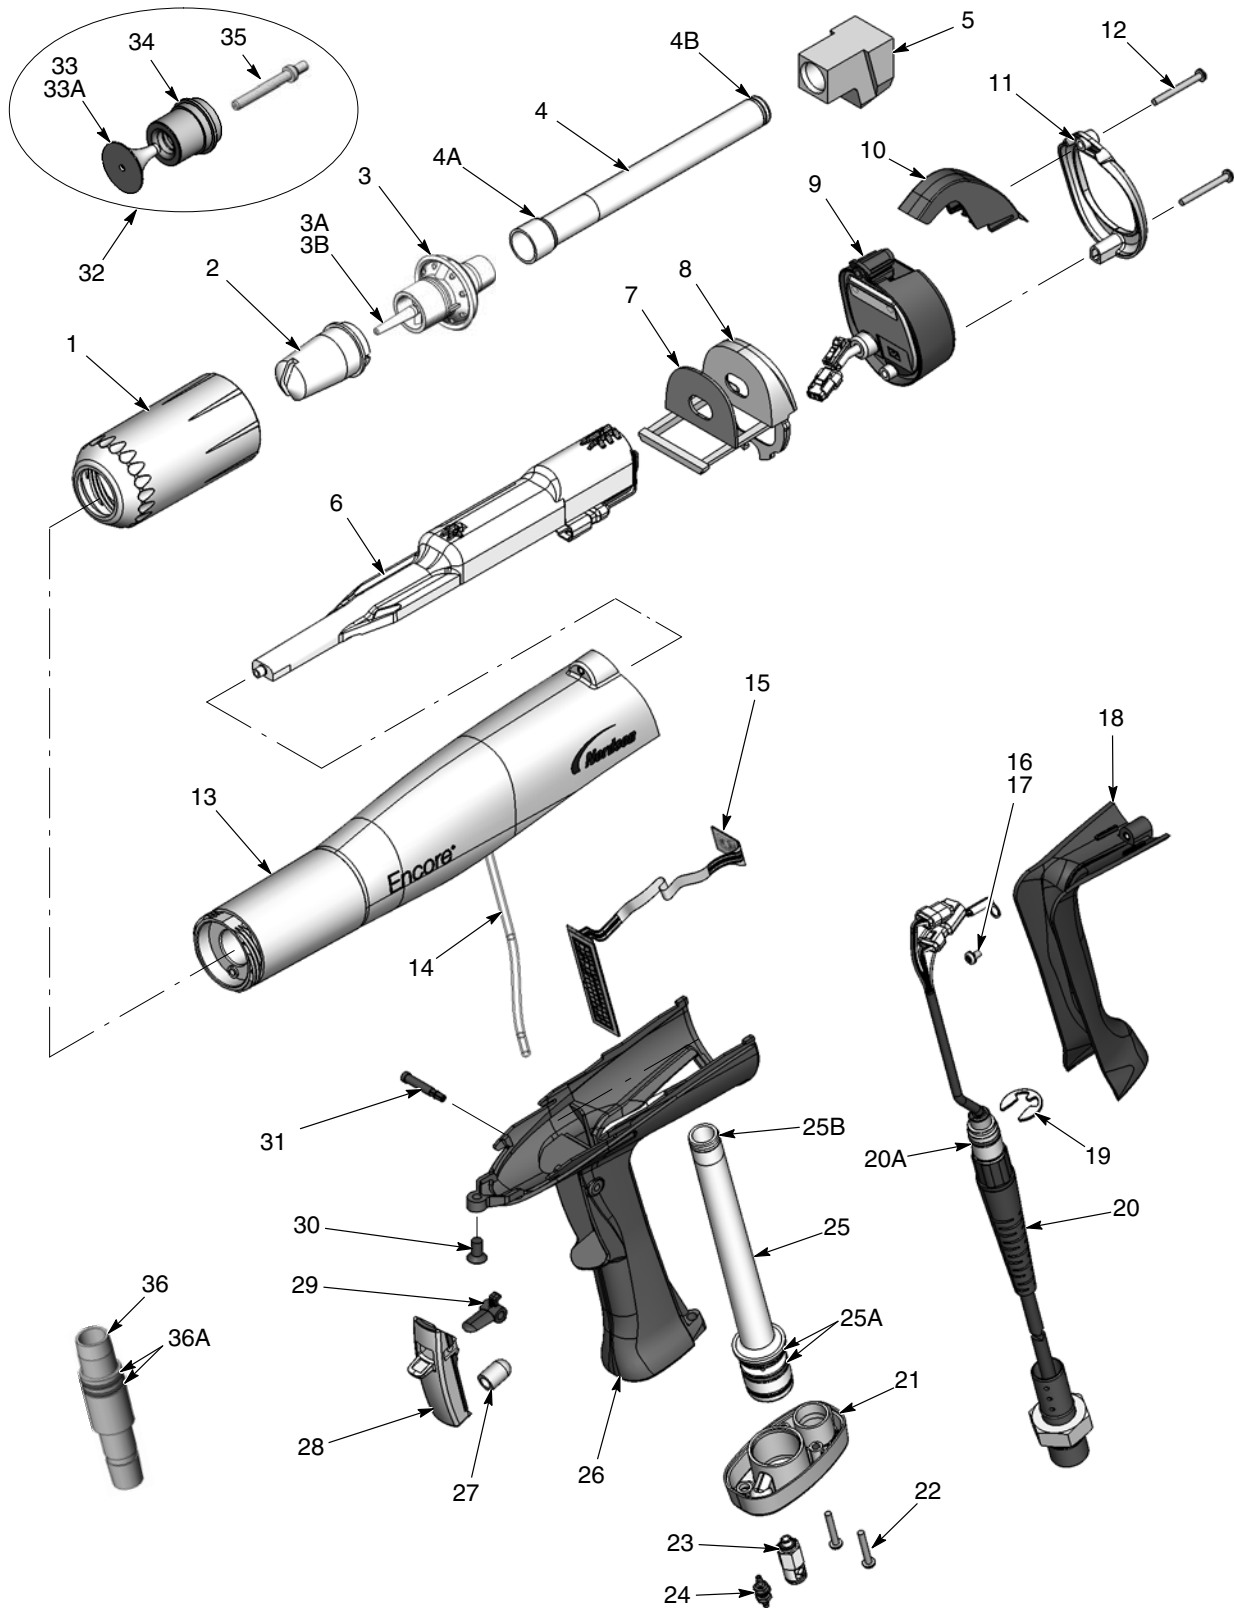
Объемный вид с разделением деталей ручного распылителя Encore XT и принадлежностей
